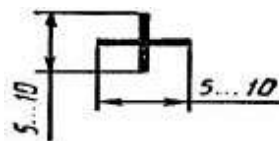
Обозначение одиночной сварочной точки
